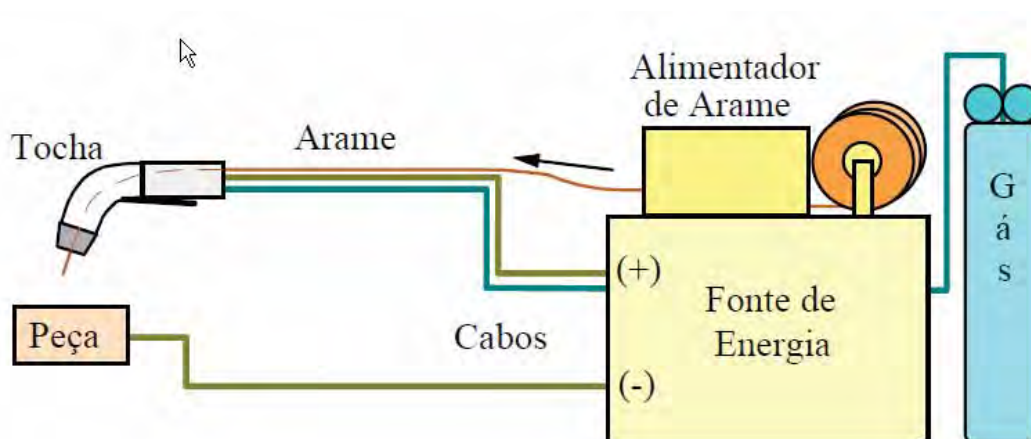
Equipamento para soldagem GMAW (MODENESE,2000).
